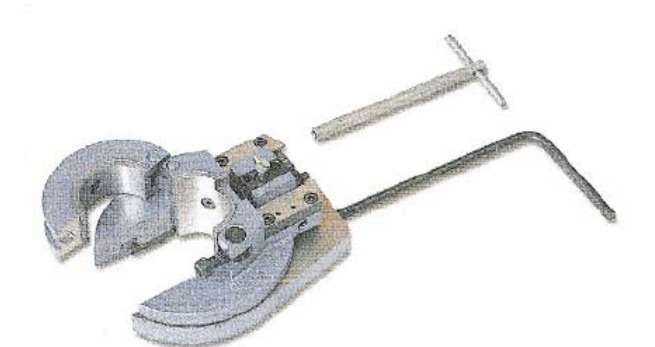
Подрезная головка для торцевания подшипников и обработки фасок.
